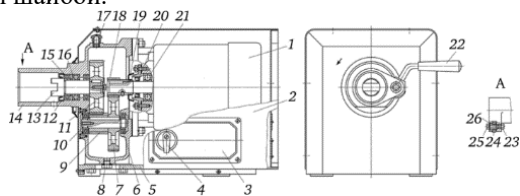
Привод П-И: 1 — электродвигатель; 2 — кожух; 3 — пульт управления; 4 — переключатель скоростей; 5 — рама; 6, 15 — шарикоподшипник; 7, 11 — колесо зубчатое; 8 — пробка сливная; 9, 18 — шестерня; 10 — вал промежуточный; 12, 20 — манжета; 13 — вал приводной; 14 — редуктор; 16 — подшипник упорный; 17 — пробка-сапун; 19 — шайба защитная; 21 — шарикоподшипник электродвигателя; 22 — рукоятка; 23 — гайка; 24 — кулачок; 25 — болт; 26 — ось.
